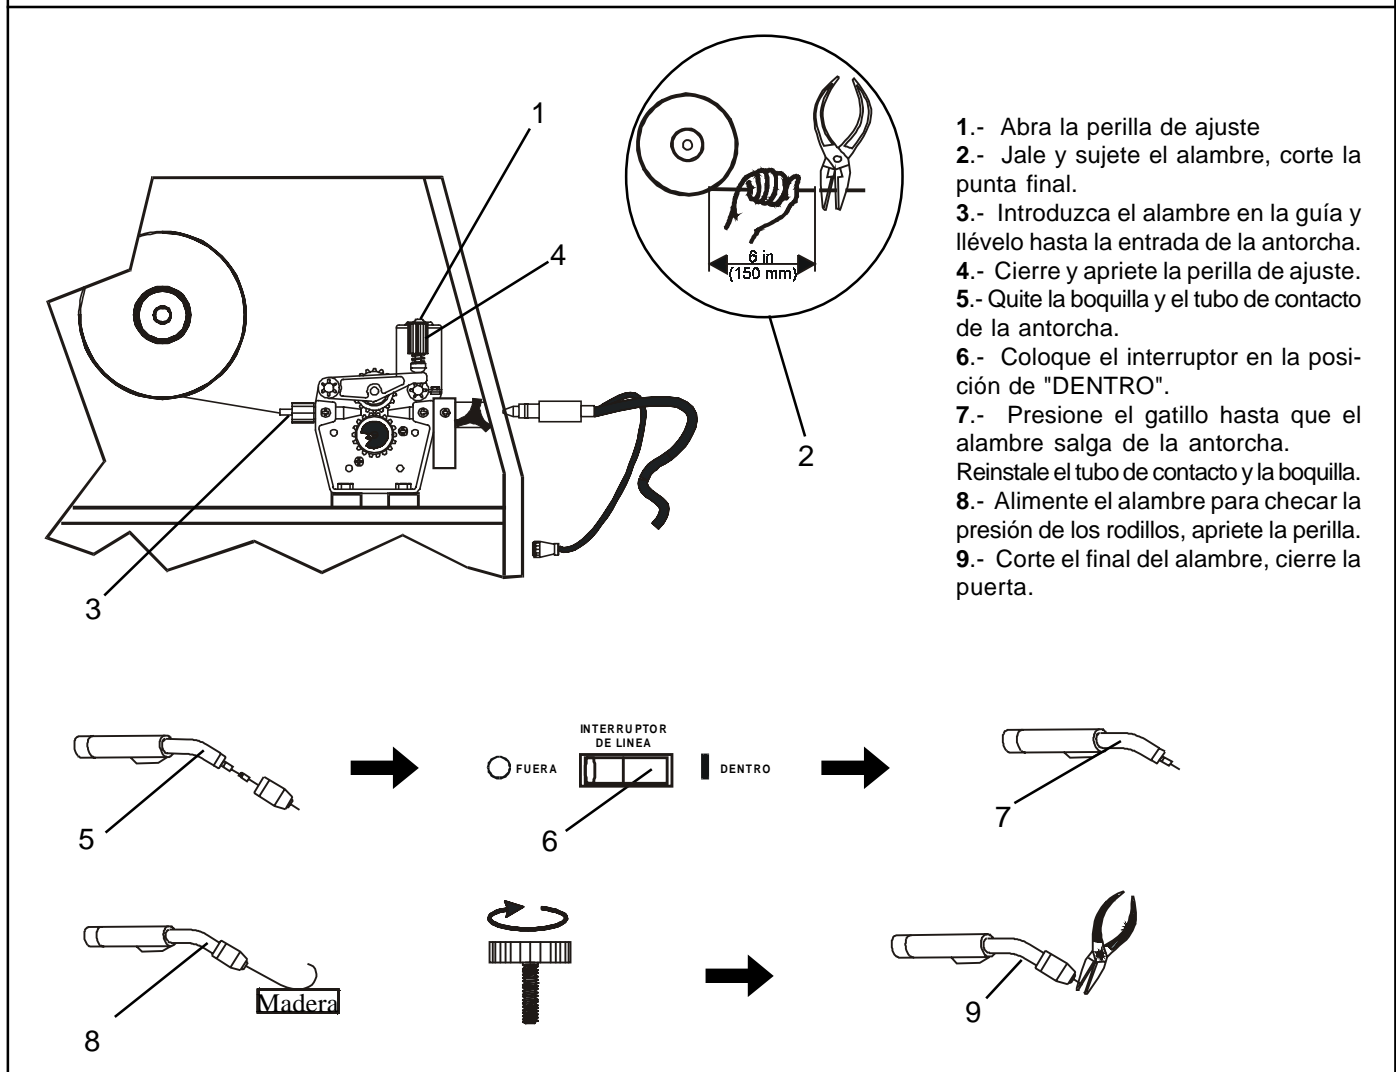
INSTALACIÓN DEL ALAMBRE DE SOLDADURA
